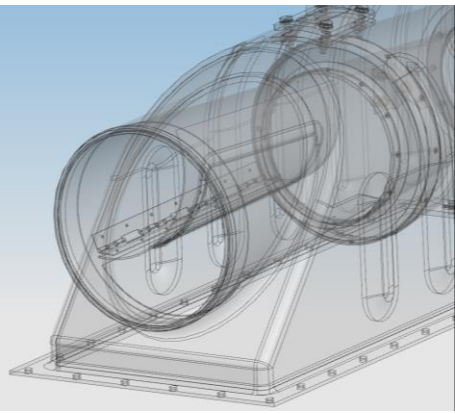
Vista Seccionada del Modelo CAD de Casting
